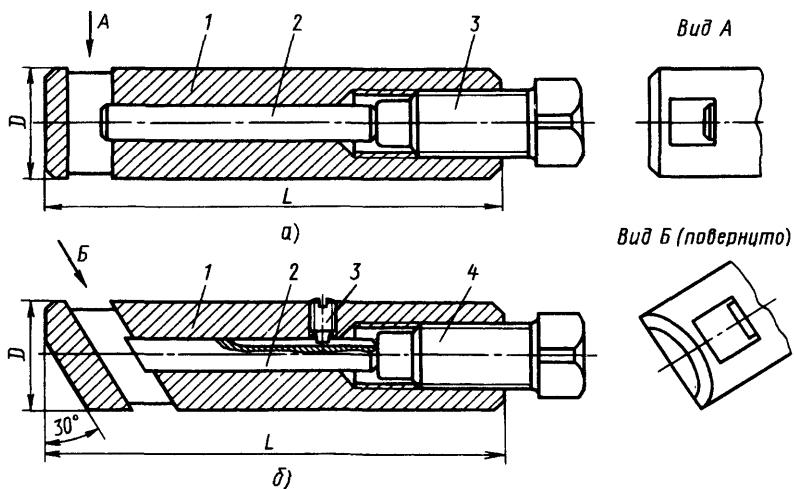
Цилиндрические державки для крепления резцов перпендикулярно (а), под углом (б) к обрабатываемой поверхности:
